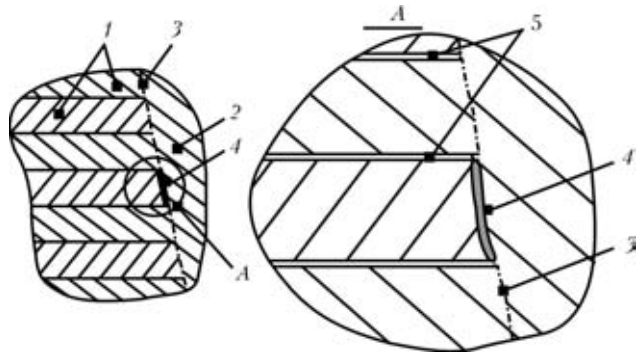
Зона відриву шару рулонної обичайки, утворена у зварному з'єднанні багатошарової посудини: 1 — шари рулонної обичайки; 2 — зона наплавленого металу; 3 — межа сплавлення основного і наплавленого металу; 4 — площинний дефект (зона відриву рулонної обичайки); 5 — зазори між шарами рулонної обичайки
